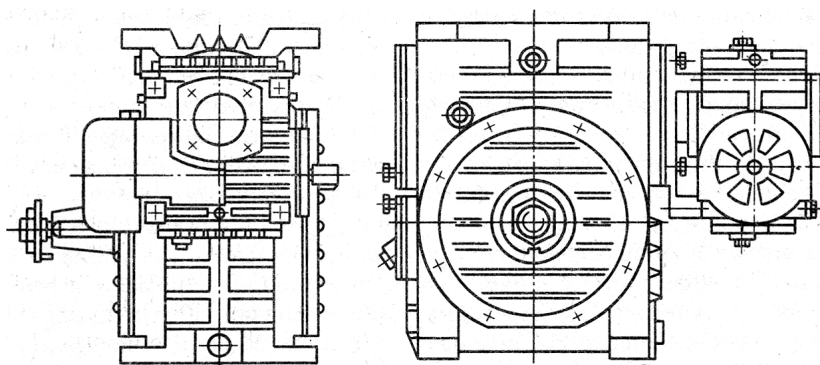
Компоновочная схема двухступенчатого червячного редуктора
